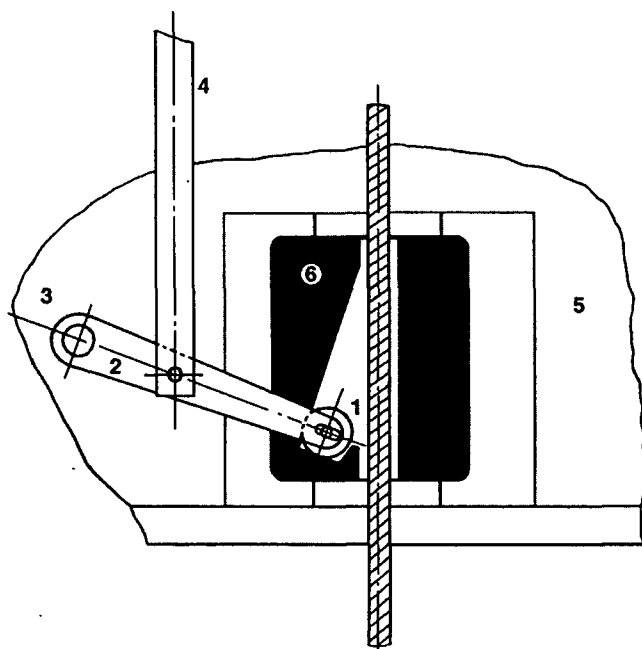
Схема роликового ловителя: 1 – ролик, 2 – приводной рычаг, 3 – общий вал, 4 – тяга управления, 5 – блок ловителя, 6 – корпус
